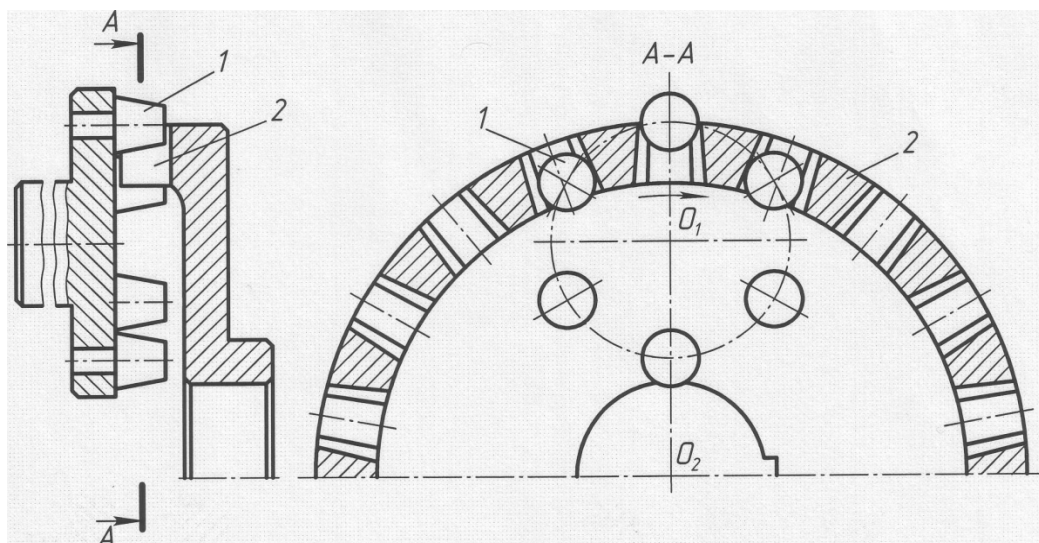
Кинематическая схема торцевой зубчатой передачи с внутренним зацеплением.
